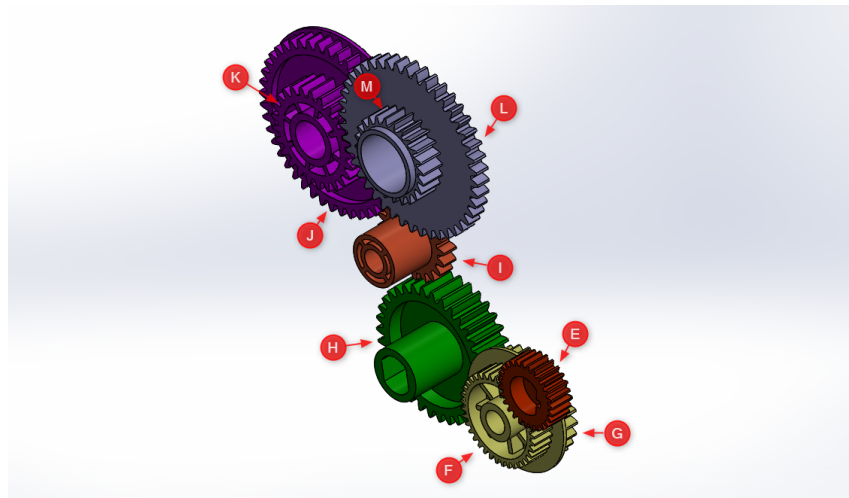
Engranaje controlador del rodillo alimentador hoja.
